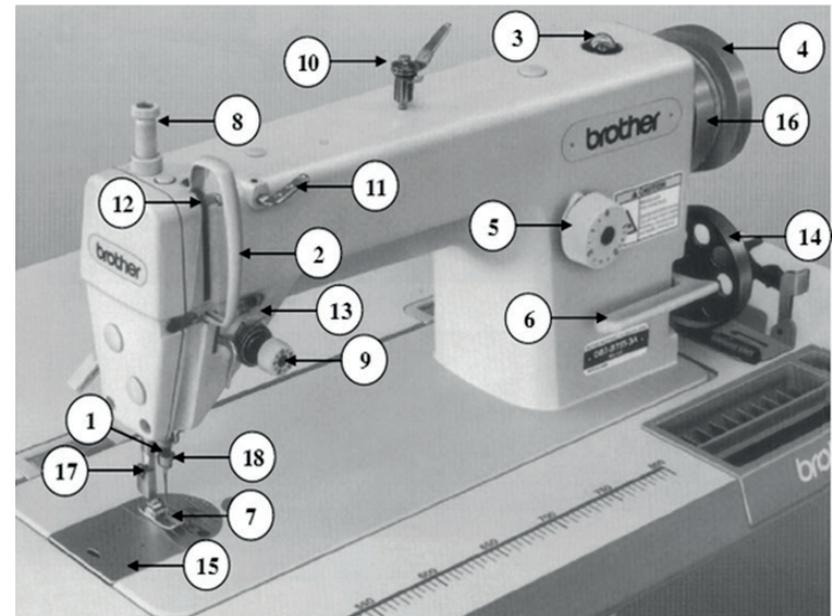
Partes de la cabeza de la máquina. Fuente: Autoría propia.
